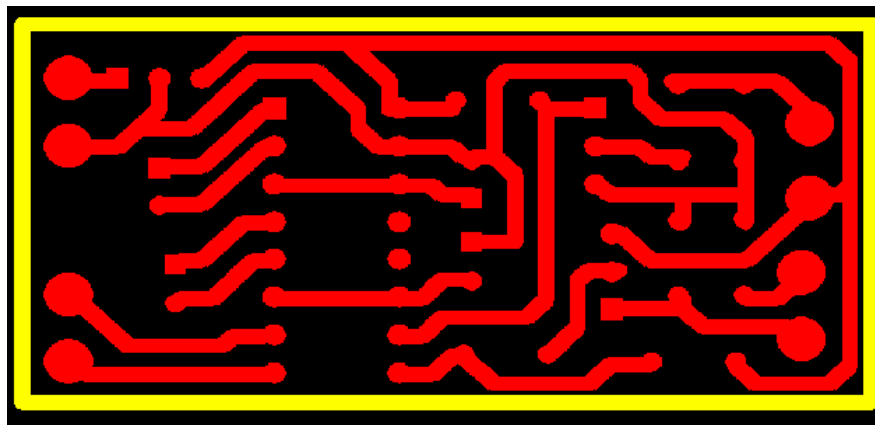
Tarjeta electrónica de la interfaz de comunicación, cara de soldadura.
